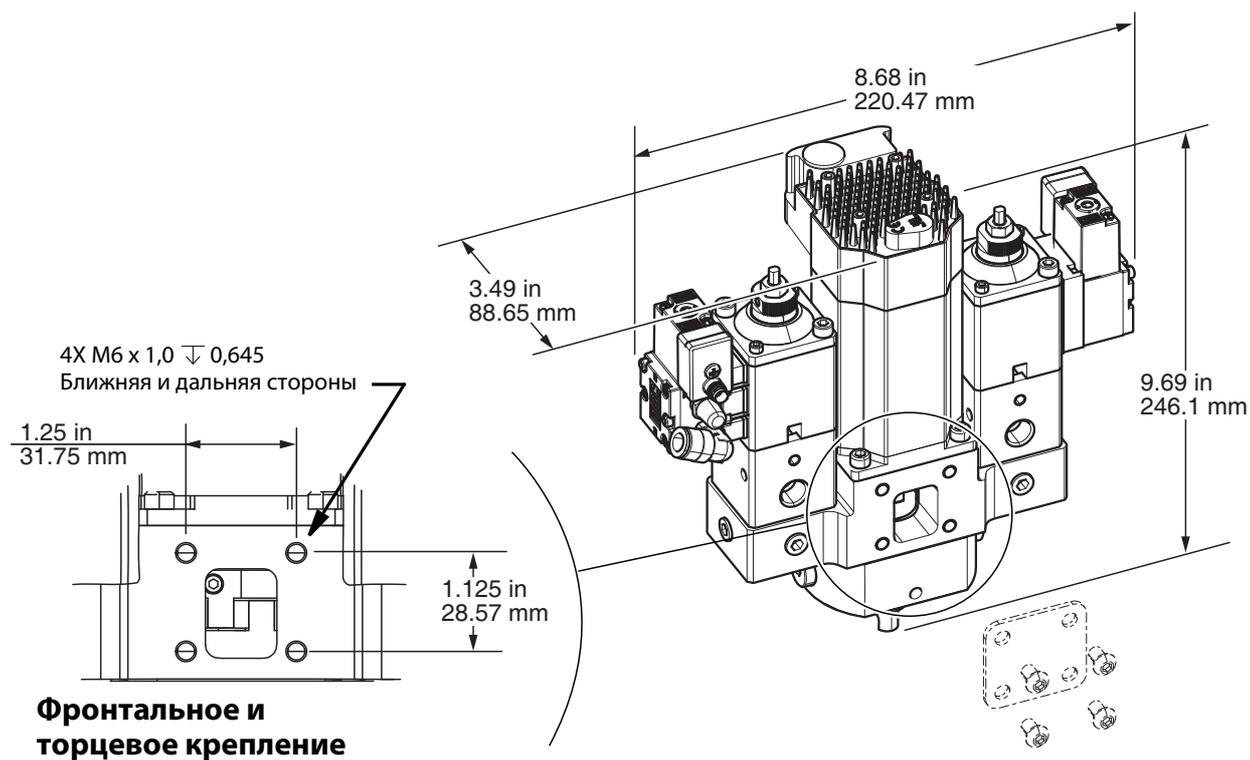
Габаритные размеры динамического смешивающего клапана Voltex
